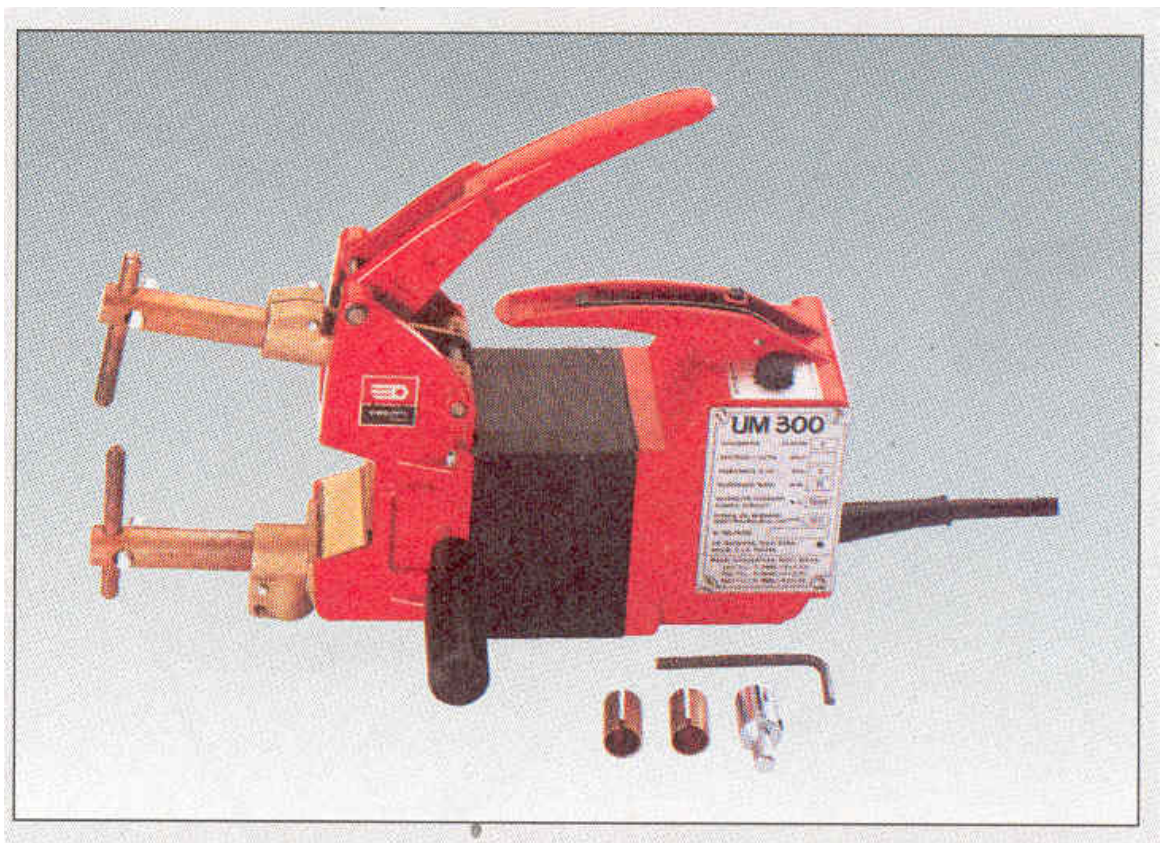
Máquina de soldar por pontos Facom UM 300
